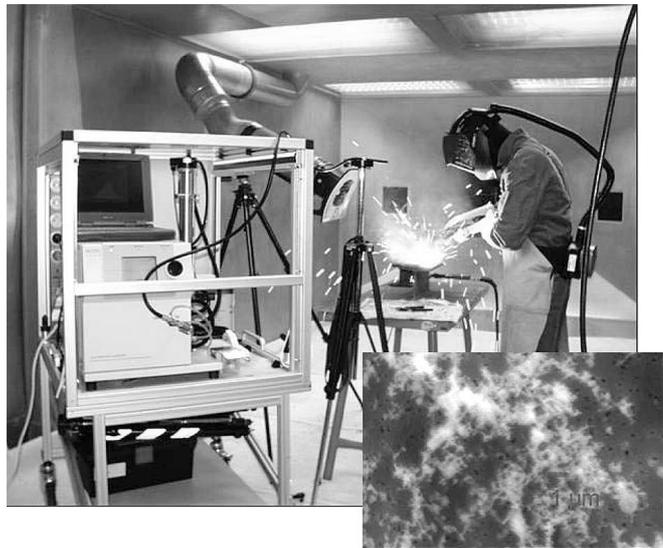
Messungen ultrafeiner Partikeln am Arbeitsplatz und Schweißrauch-aerosole.
